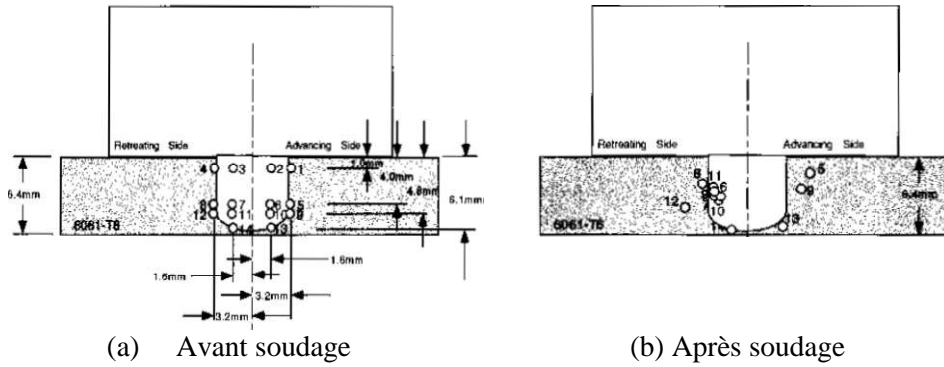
Configuration des marqueurs : de type billes placées autour du pion avant et après le soudage [Colligan 99].
